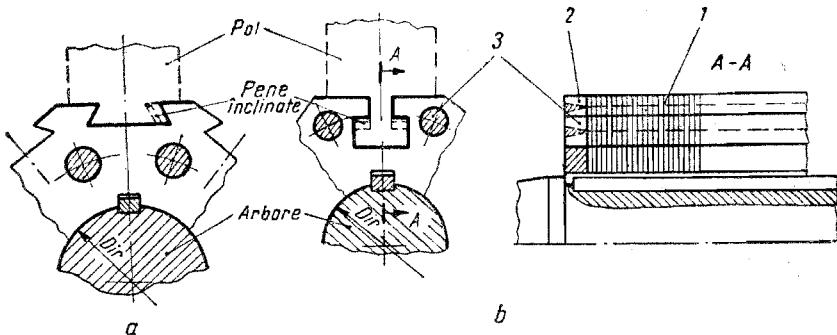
Butuc rotor pentru mașina sincronă :
